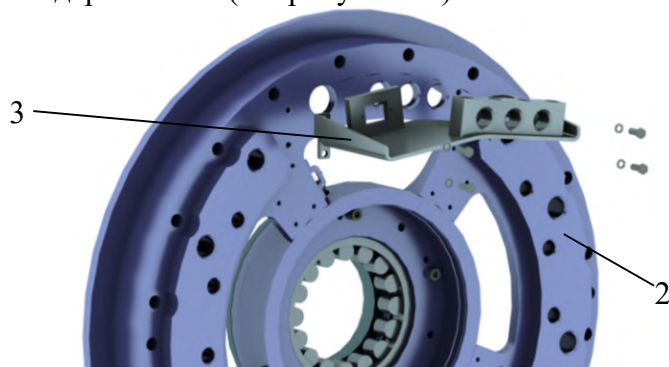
Демонтаж держателя со щита подшипникового (сторона тормоза)
